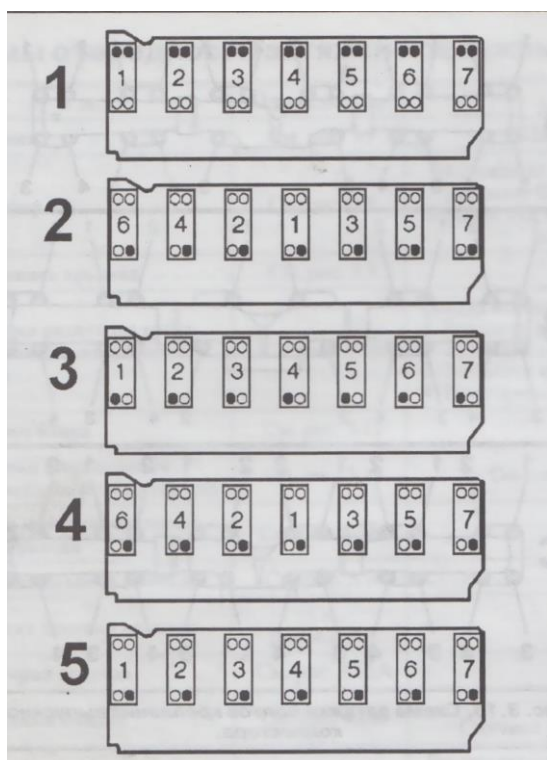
Схема затяжки крышек распределительного вала двигателя D12C
